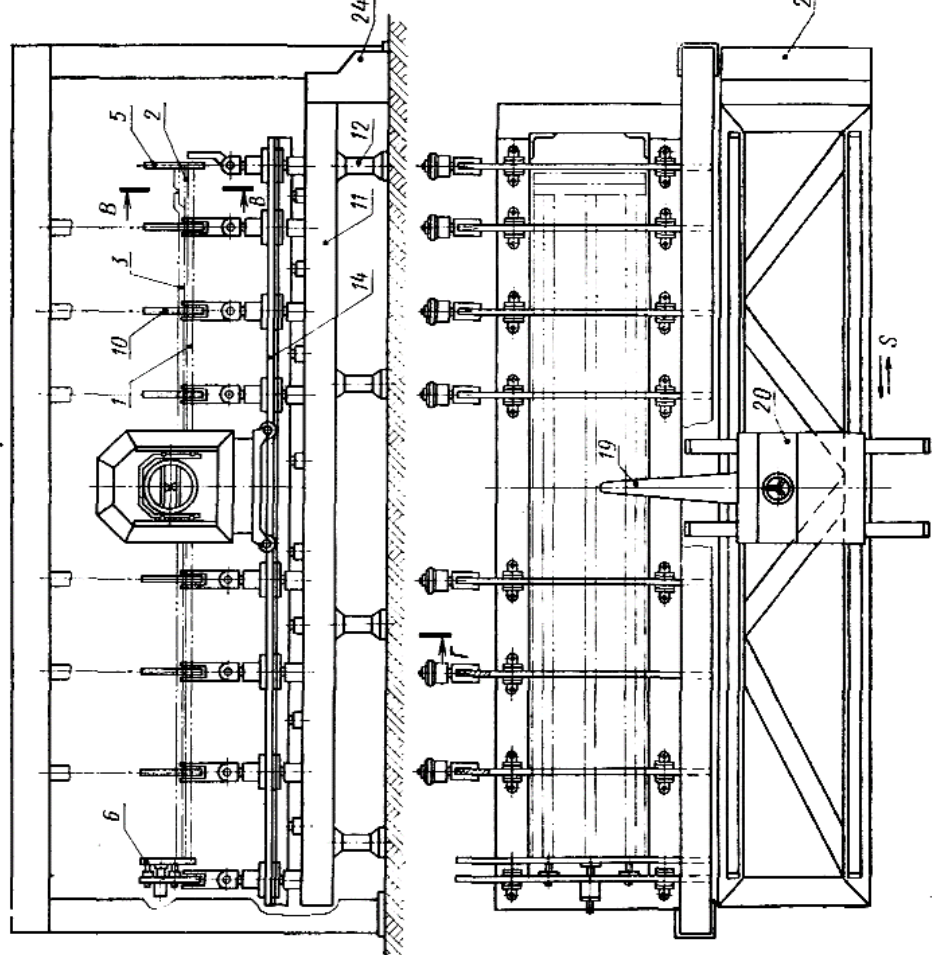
Компонентный чертеж сборки и сварки панели
